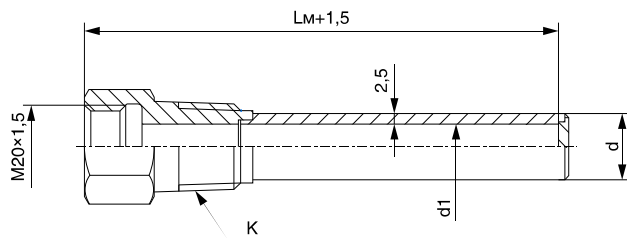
ГТ-711 с конической резьбой для ДТ с неподвижным штуцером
